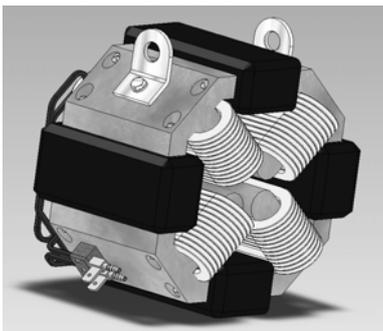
Общий вид квадрупольного магнита второго оборота рециркуляции
